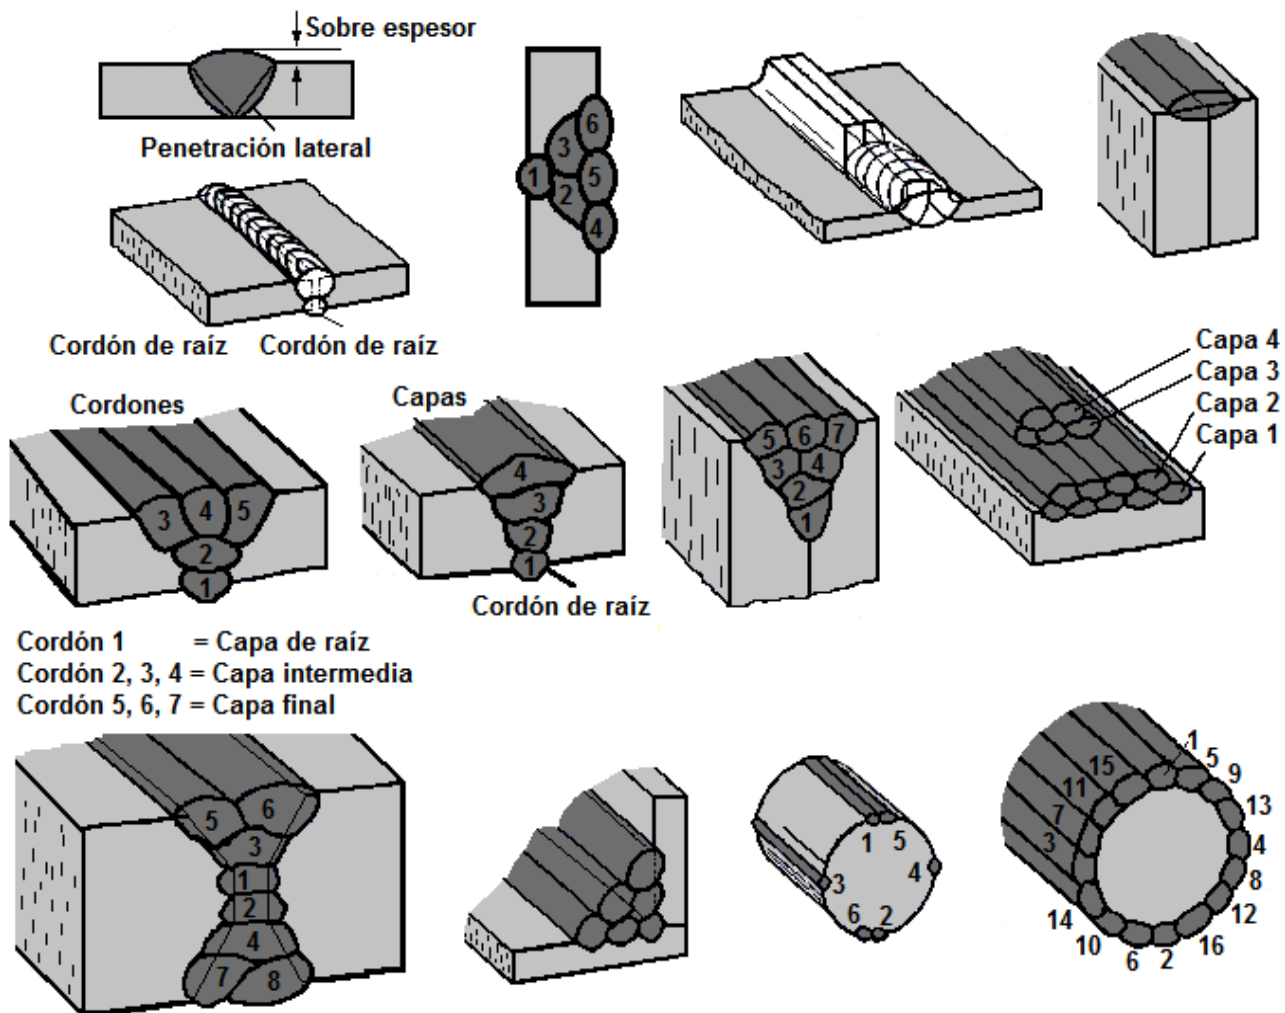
Construcción de la soldadura y el orden de los cordones (28)
